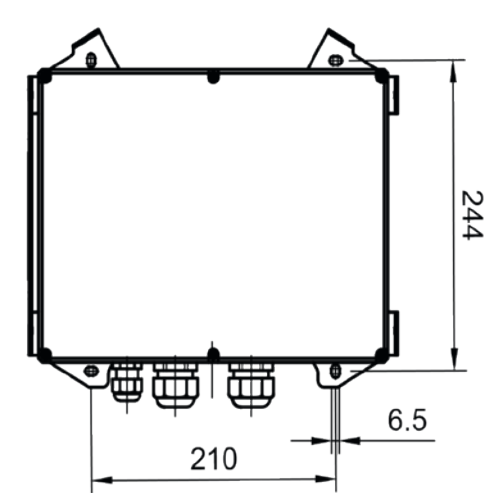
Frontalansicht Wallbox ohne Designhaube
